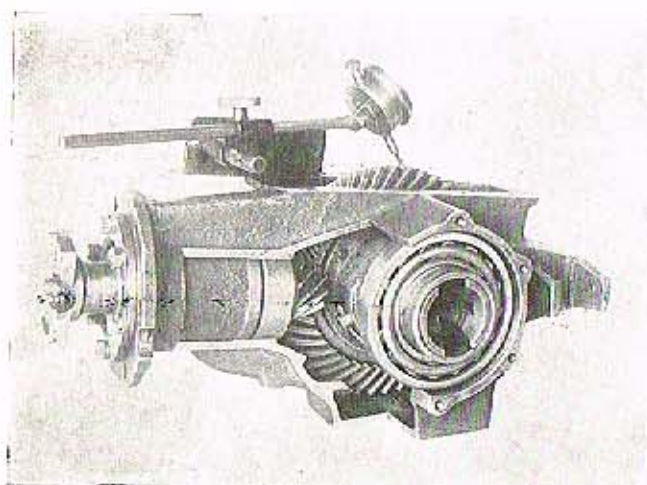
Měřidlo vložené do skříně zadní nápravy.
